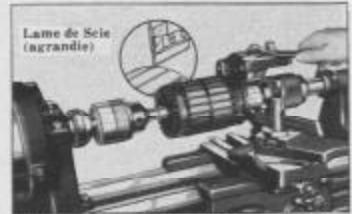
Rectification et Dégagement d'un Collecteur d'Induit
